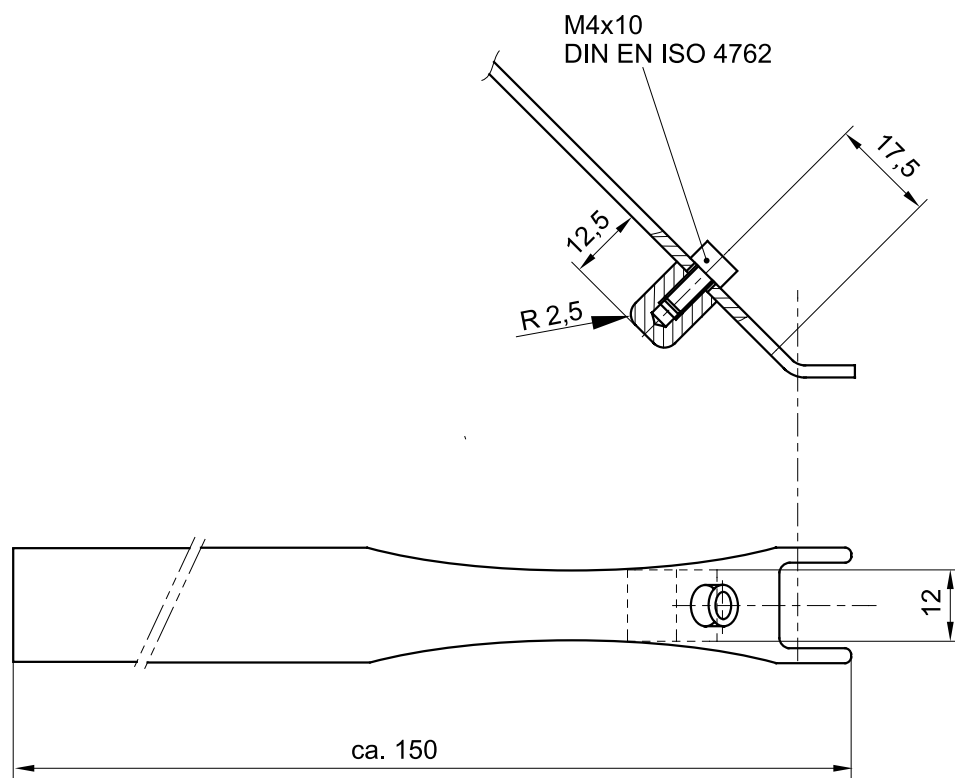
Werkzeug zum Lösen der Kabelstecker von den Magnetspulen
